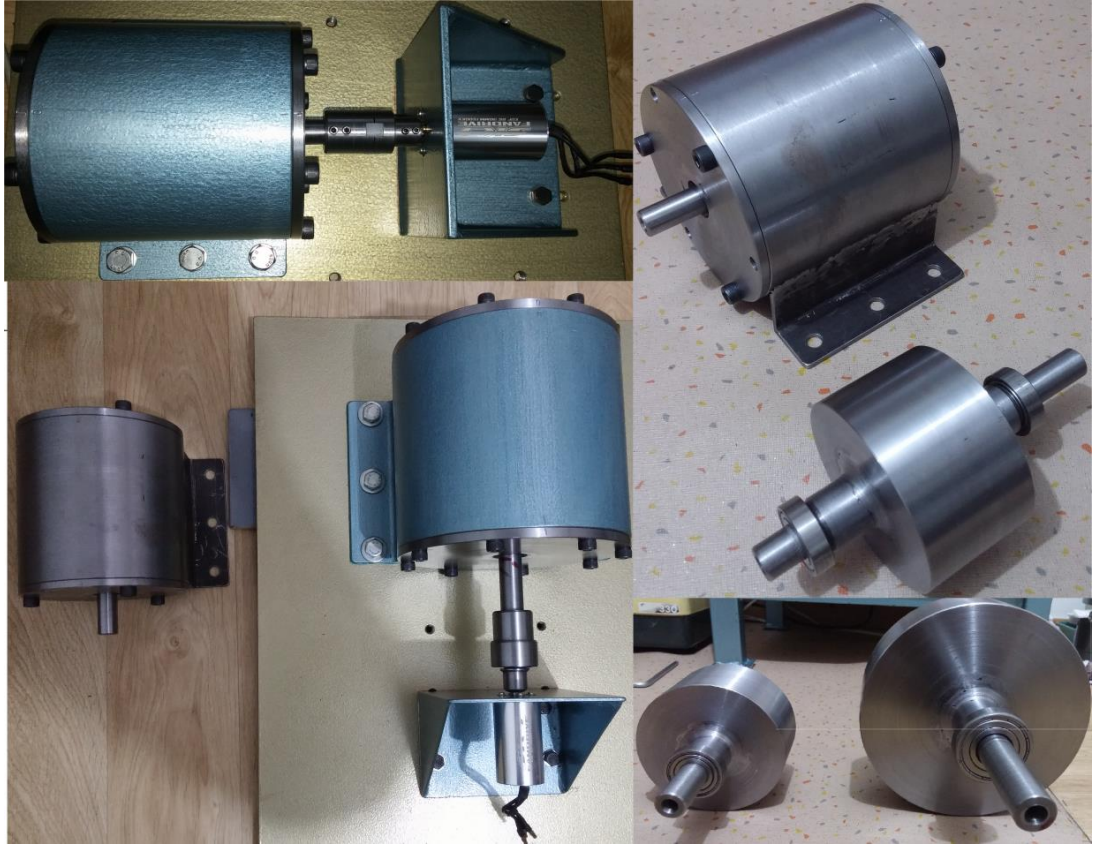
VEDS'in mil ve rulman montajları yapılmış olan rotor kısmı
